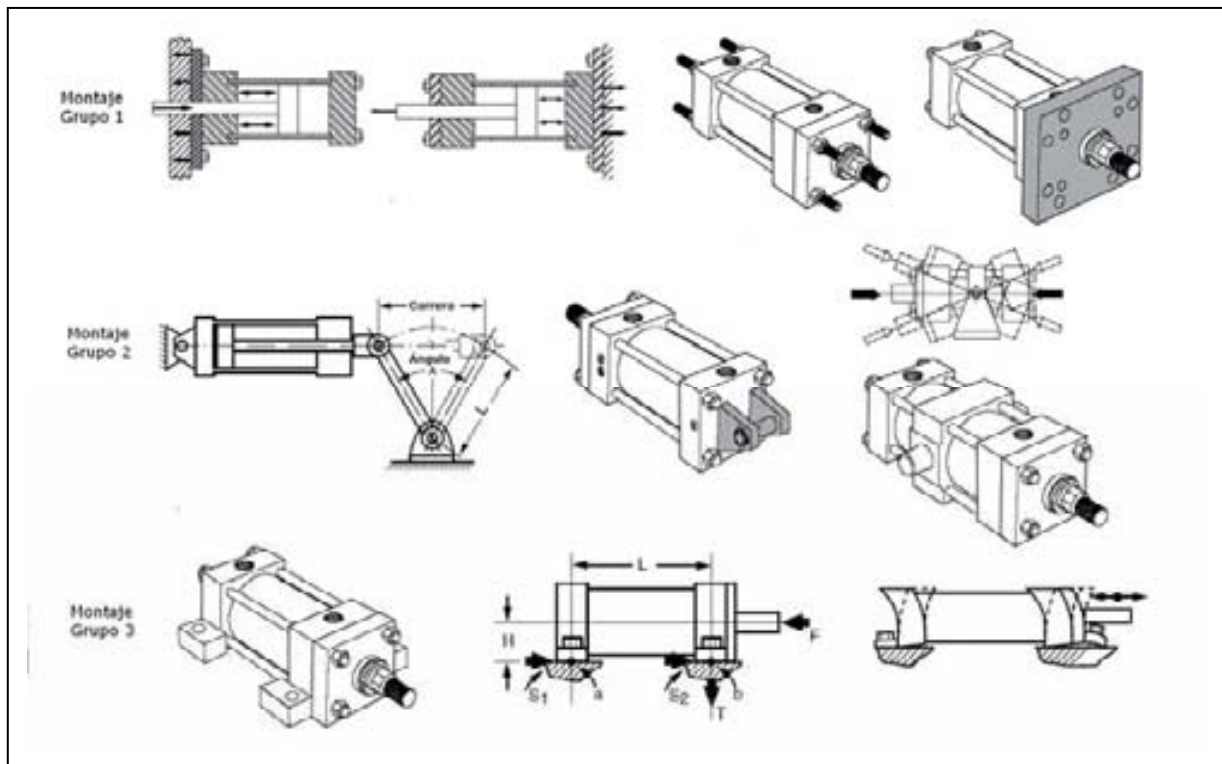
Tipos de montajes de cilindros. Fuente: Parker Hannifin Corporation
